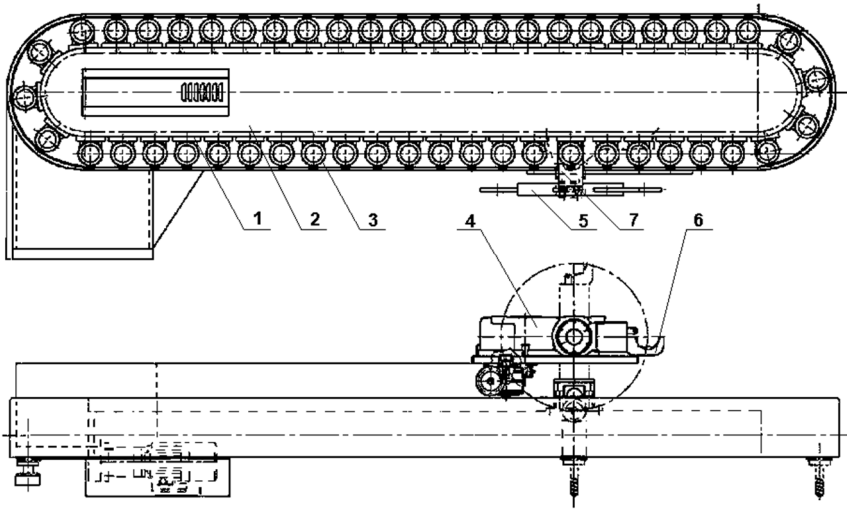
Пристрій АЗІ СТА компанії COLOMBO FILIPPETTI з ланцюговим інструментальним магазином і автооператором: 1 – інструментальний ланцюг, 2 – корпус, 3 – інструментальне гніздо, 4 – привід автооператора (АО), 5 – рука АО, 6 – захват АО, 7 – позиція перевантаження
